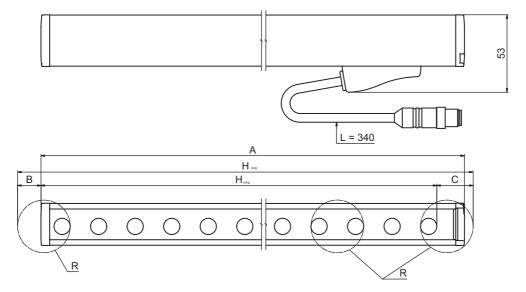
Dimensions de l'émetteur Guest et du récepteur Guest
